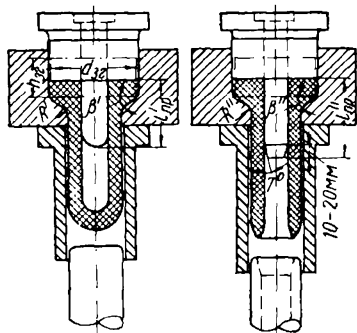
Схема двухпереходной штамповки поковки со сквозным отверстием
